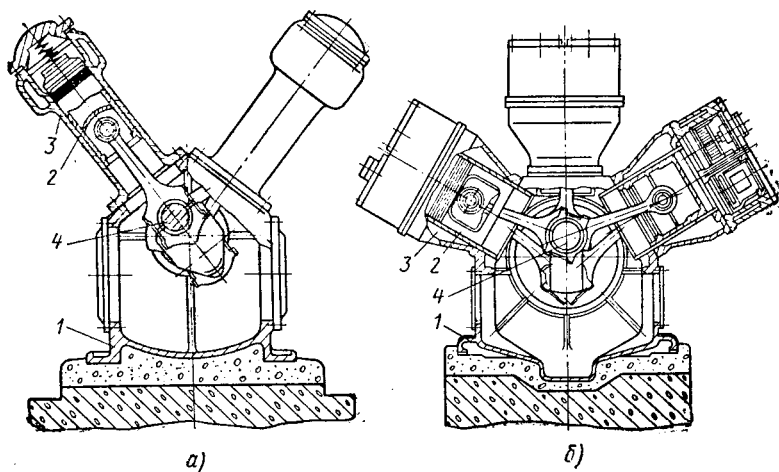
Угловые У-образный (а) и УУ-образный (б) компрессоры: 1—рама-картер; 2 — поршень; 3 — цилиндр; 4 — коленчатый вал
